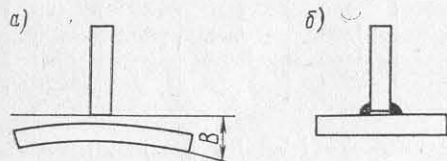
Форма обратного выгиба узлов набора перед сваркой (а) и тавровое соединение после сварки (б).
